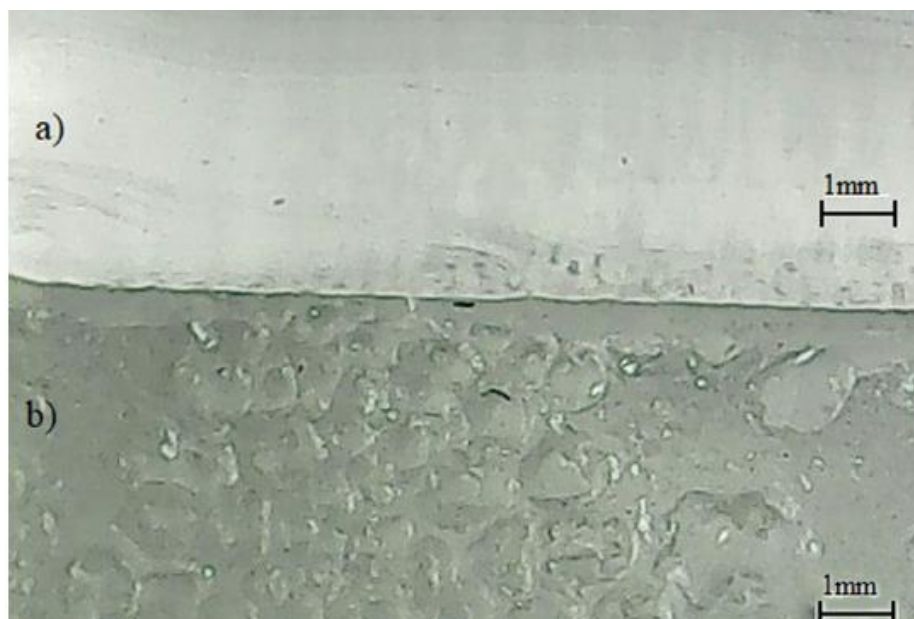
Condição dos moldes no processo de desmoldagem.
